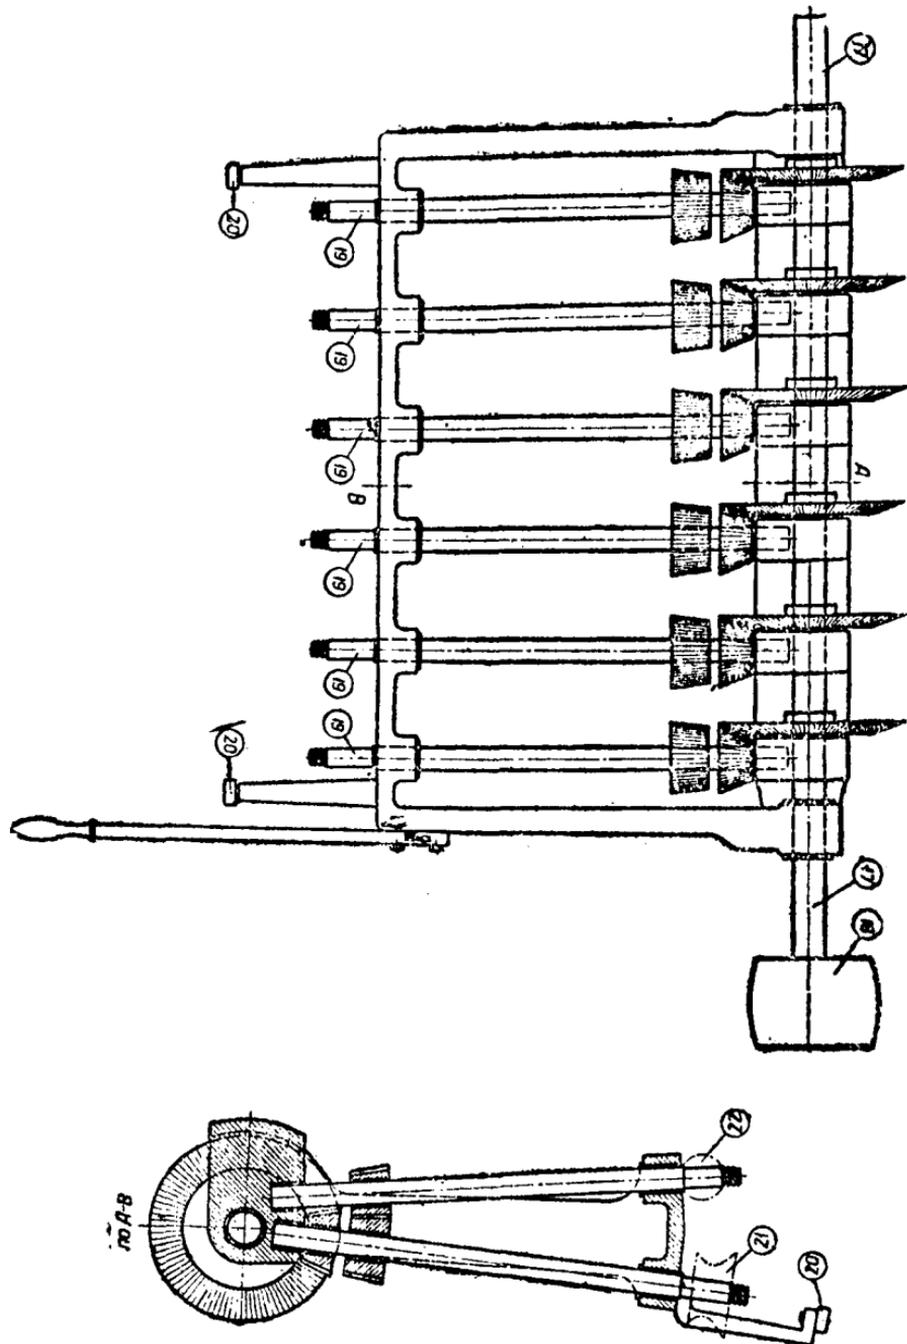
Качающийся кронштейн станка т. Пурепкого для операций 2-й и 3-й. 17—конец вала, вставляющийся в подшипник станины; 18—шкив для ремня контривода; 19—концы вала для надевания фр.з; 20—ролик, 'катящийся по копиру приспособлений при обработке спинки ложки; 21—фрезы для спинки ложки; 22—фрезы для лунки.
